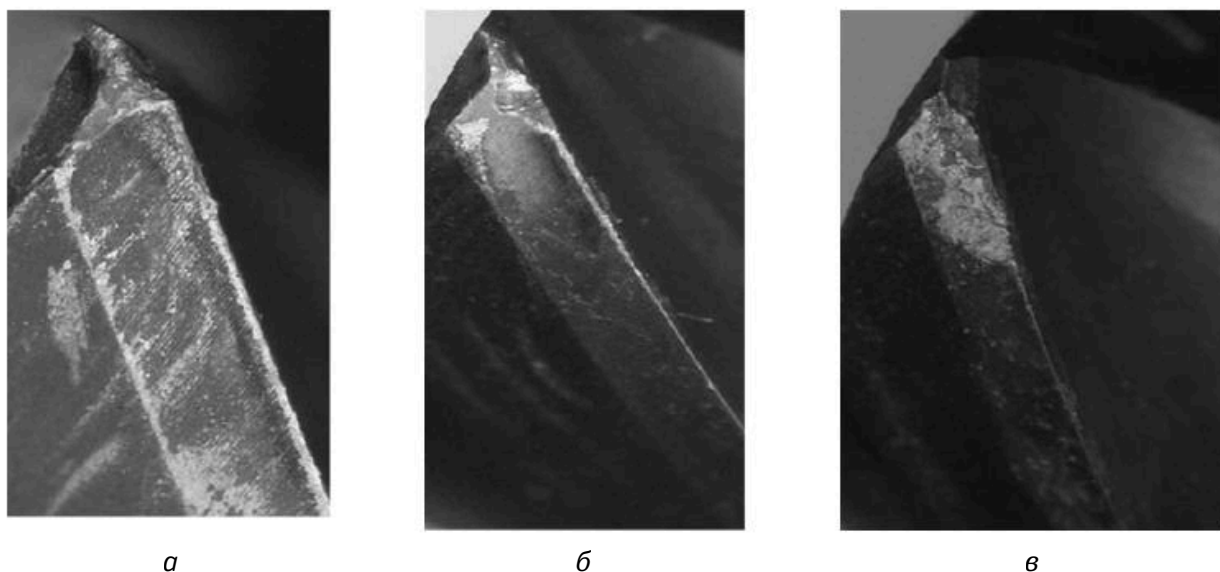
Состояние режущих зубьев испытываемых фрез:
